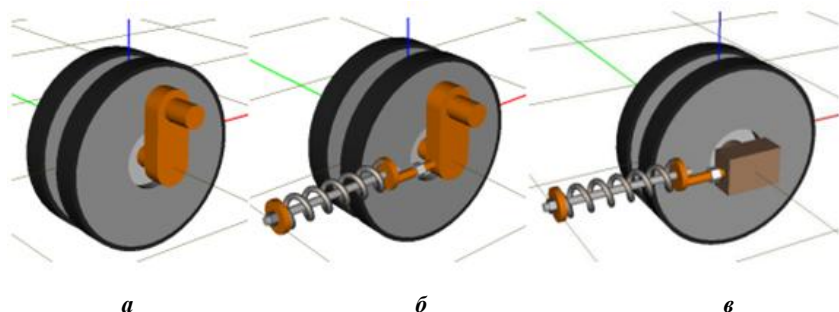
Стандартные модели направляющих колес с натяжным устройством:
